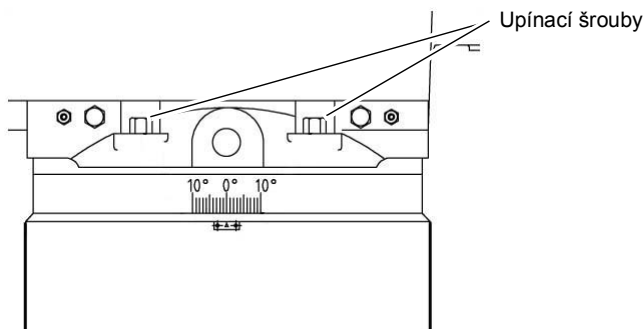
Pohyb unašeče frézovací hlavy vpřed / vzad
